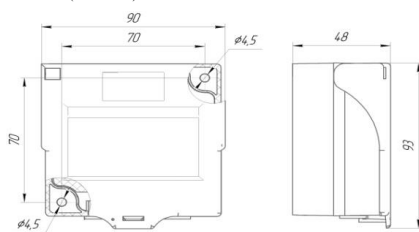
Dimensiuni generale și de instalare ИПП-1
